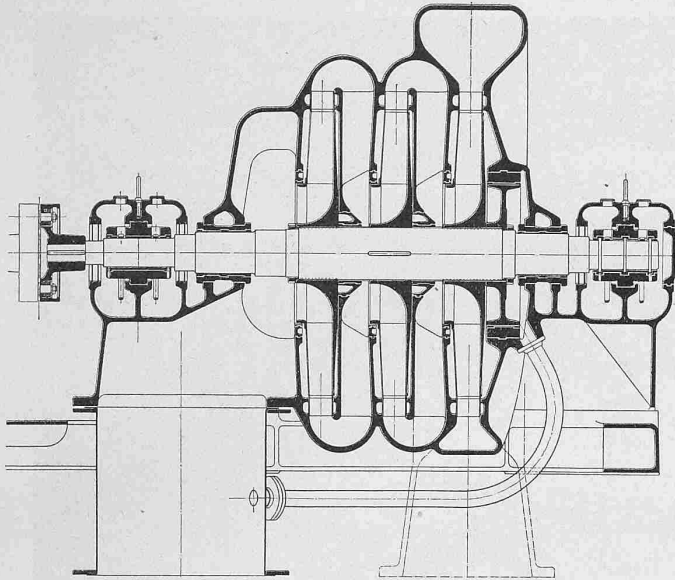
Gasgebläse für 700 m³/min bei 1700 mm W.S.; 3000 Uml./min.
